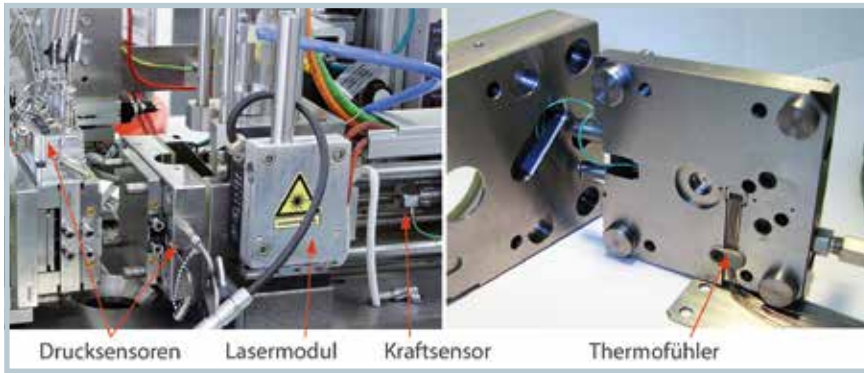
In die Mikrospritzgießmaschine und ins Werkzeug sind mehrere Sensoren integriert, um die Prozessparameter zu erfassen
